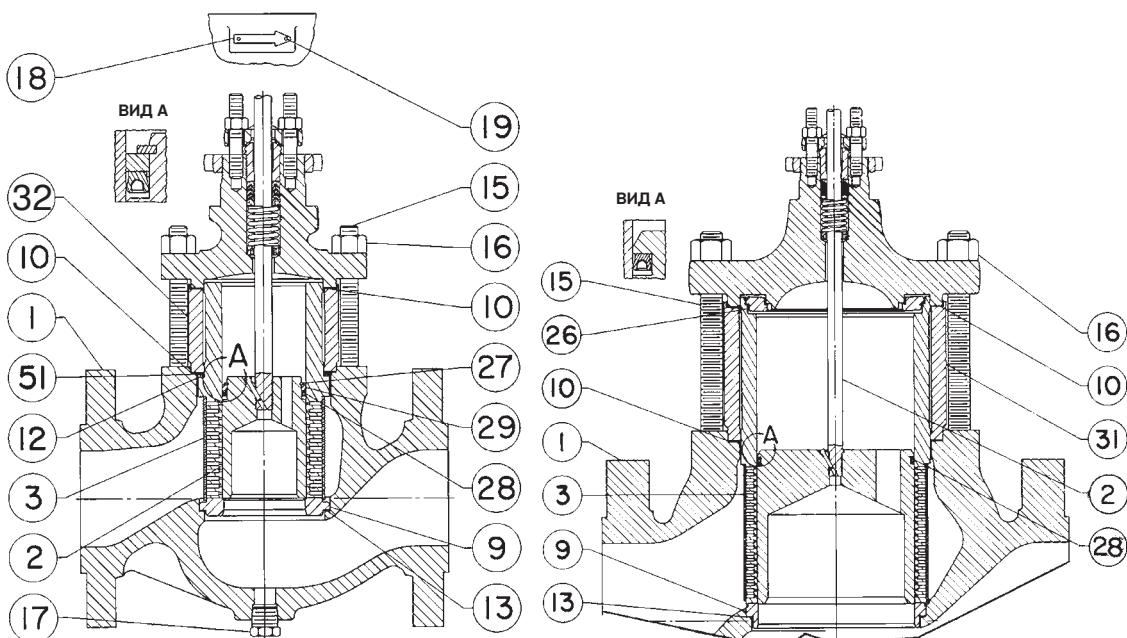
Детали клапанов Cavitrol III и Fisher ET для номинального размера трубы 8 дюймов с дополнительной сливной заглушкой
